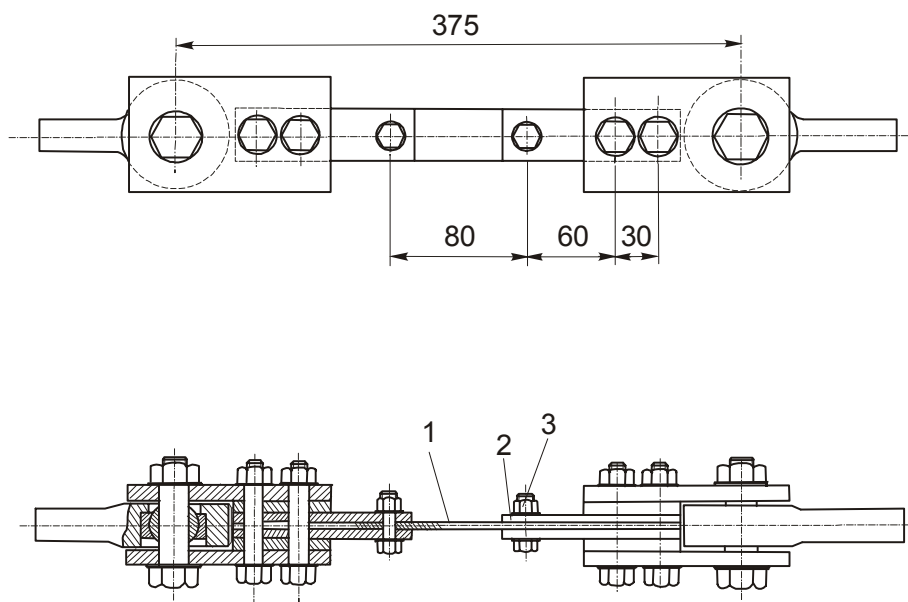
Приспособление для исследования усталостной долговечности одноболтовых срезных соединений из титанового сплава ВТ6:
